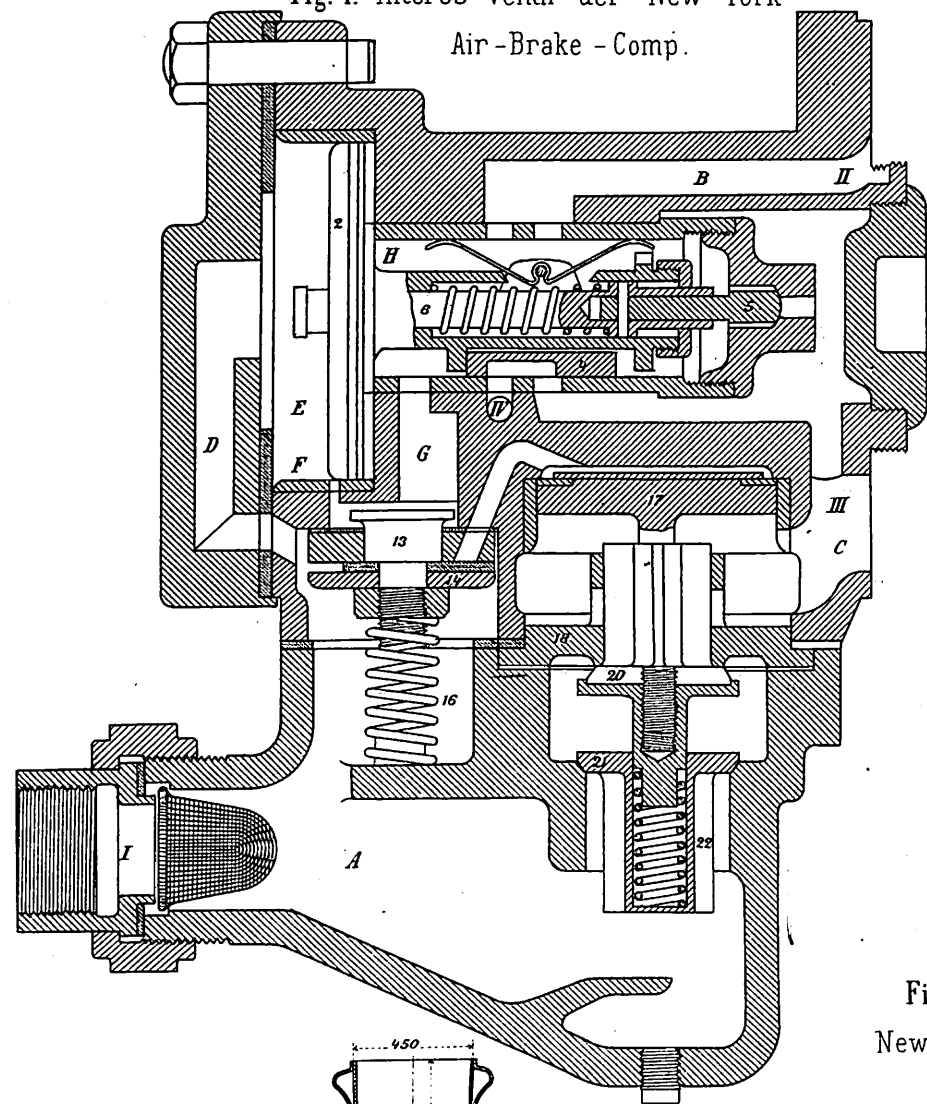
Anstellventile für Luftdruck-Schnellbremsen.
